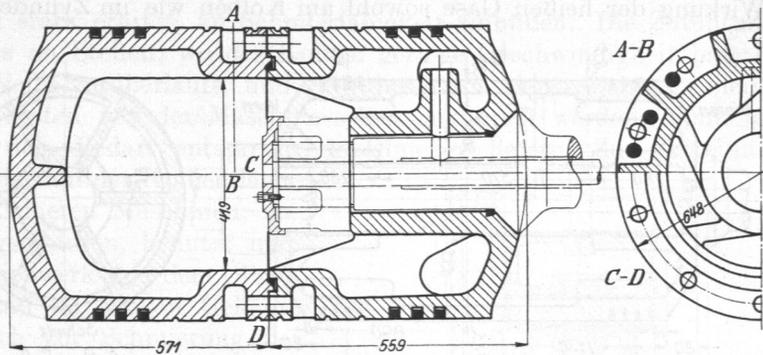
Geteilter Großgasmaschinenkolben der De la Vergne Machine Co., New York.
